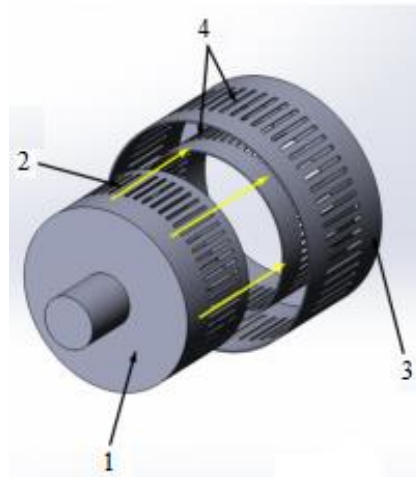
Конструкція системи ротор-статор в робочій камері РПА
